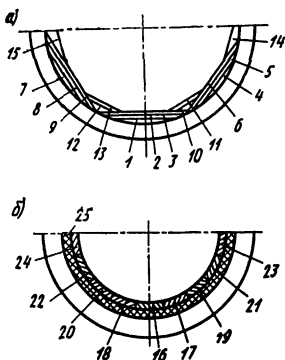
Схема наплавки баббита (а) и доплавки (б) на утонченный слой
